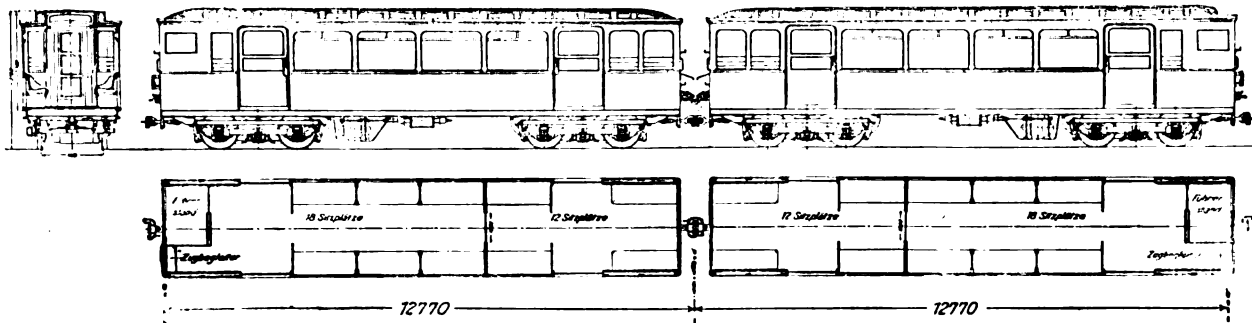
Treno della Metropolitana - Elevazione e pianta.
